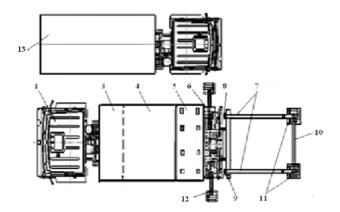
Вид сверху на передвижную ремонтную мастерскую с разборной конструкцией и разбираемым автомобилем: 1 – базовый автомобиль MA3-631705-370;
